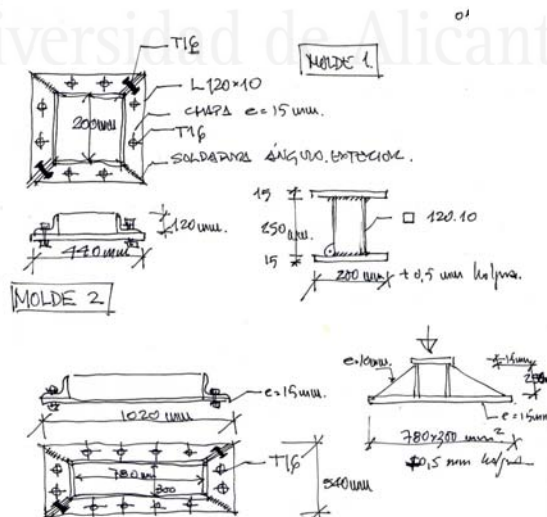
Diseño de molde de 200x200x120 mm y de molde de 780x300x120 mm.
